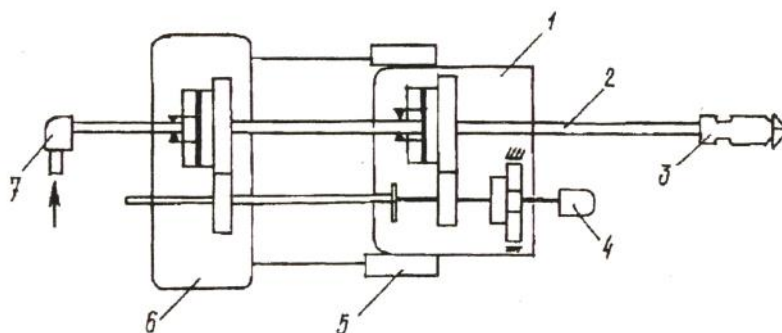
Принципиальная схема конструкции станка НКР —100:
